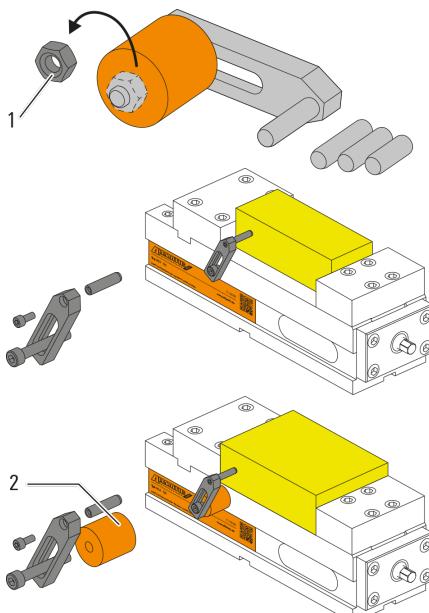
Упор обрабатываемой детали 692 168 5670 042
